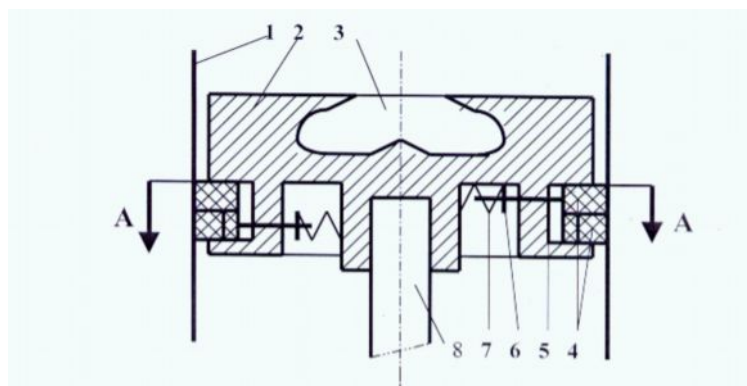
Конструкция поршня с уплотнением сухого типа:
